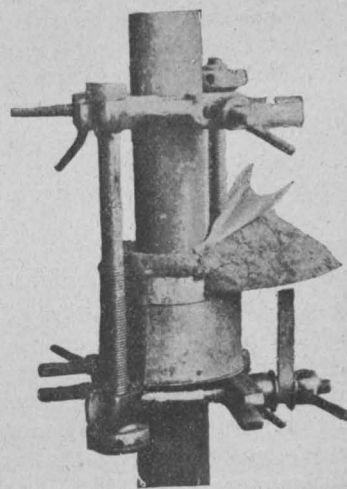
Form mit seitlicher Einlauffrinne für Rohrschweißungen bei senkrechter Lage der Rohre (fertig zum Eingießen).
